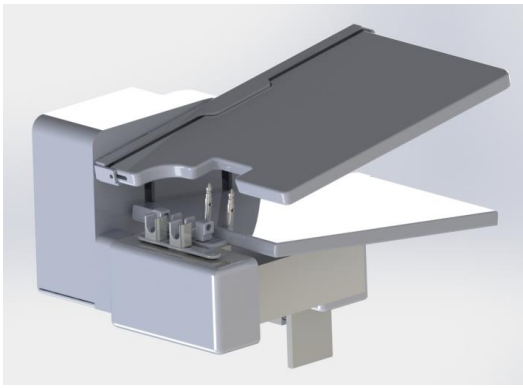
3D model sistema za filtraciju krvi - pozicije platformi za postavljanje i uklanjanje kesa sa krvlju.
